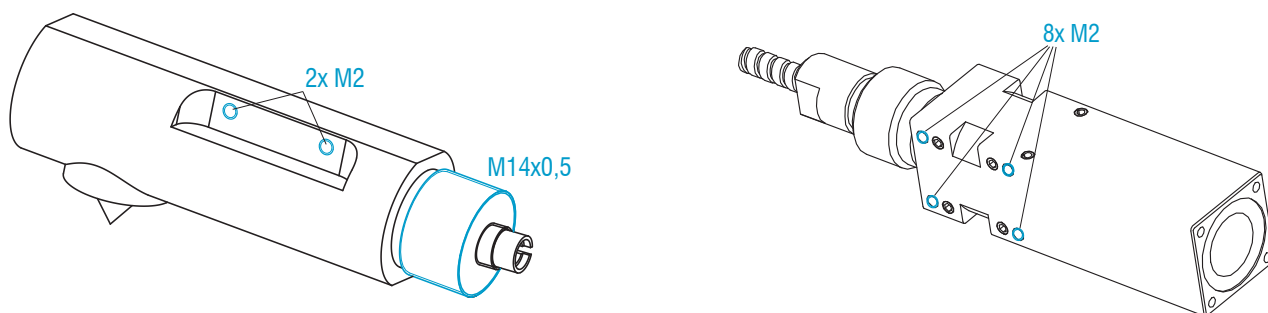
Montage für Sensoren der Serie IFS2407/90-0,3 / IFS2407-HT
